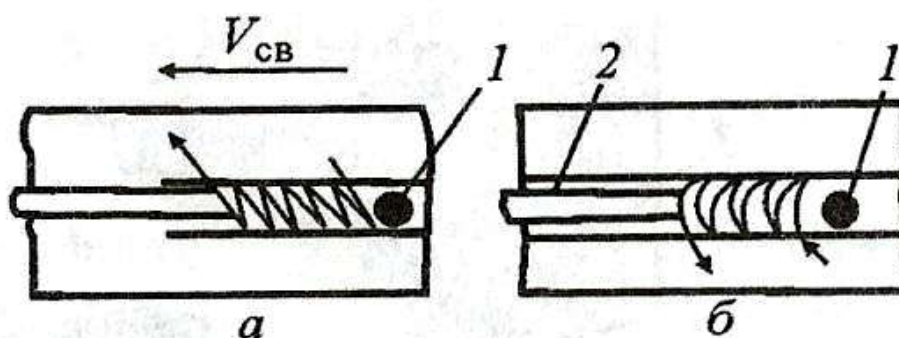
Схема подачи присадочного прутка в зону дуги при сварке тонколистового металла без разделки кромок (а); с разделкой кромок (б)
